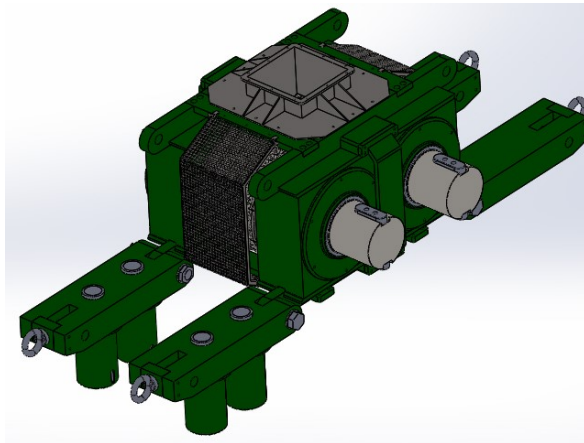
Vigas verticales en posición horizontal (Fuente: propia)
